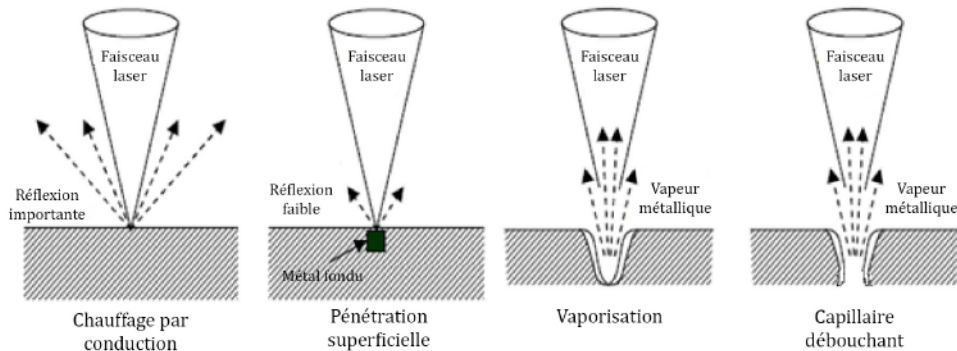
Schéma de soudage laser continu en mode keyhole
